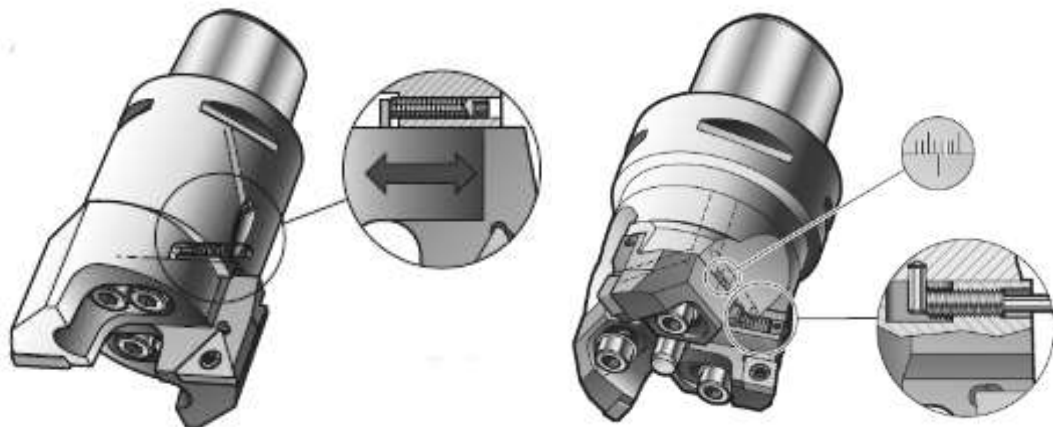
Типова конструкція різцевої головки для ступеневого розточування із регулюванням гвинтом
